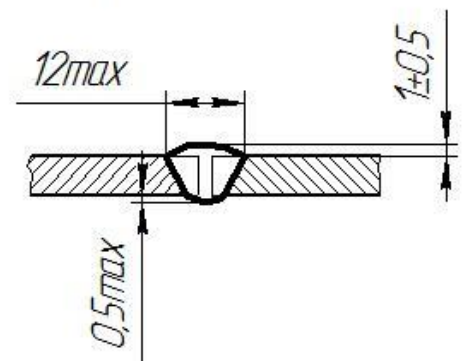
Подготовка кромок и форма шва под сварку
